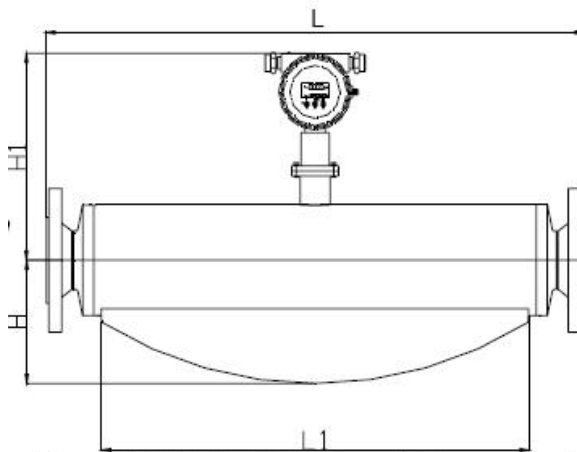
Габаритный чертеж прямотрубного сенсора
